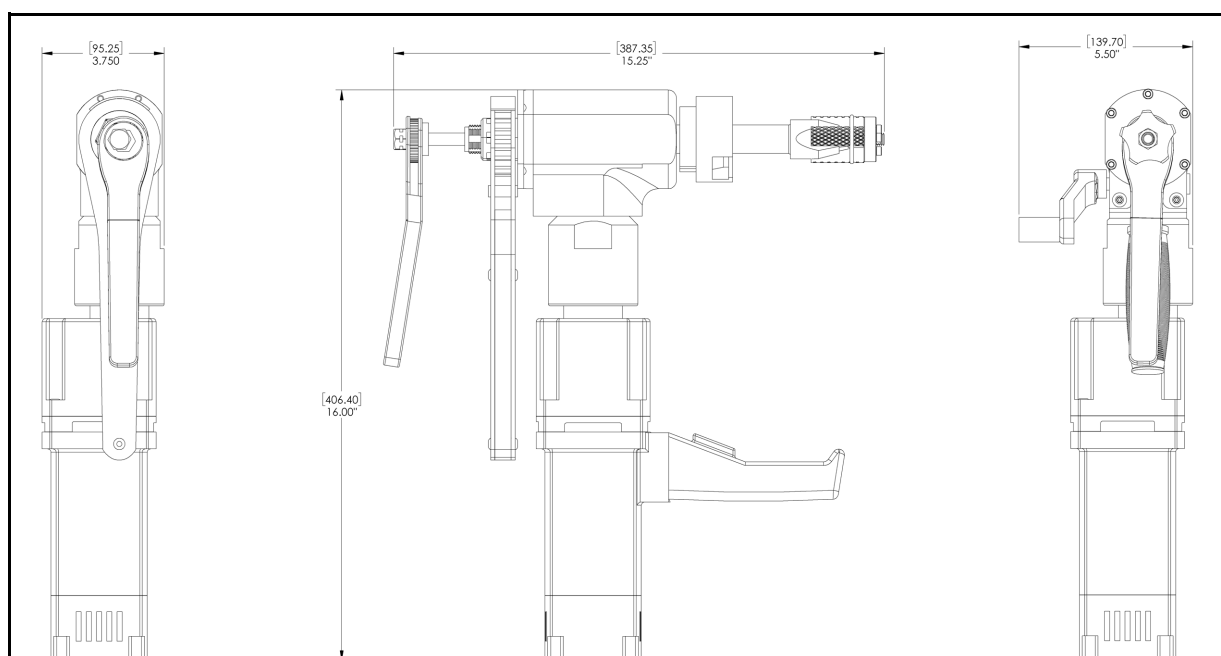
DIMENSIONS DE LA BG44 BOILER GUN ÉLECTRIQUE
